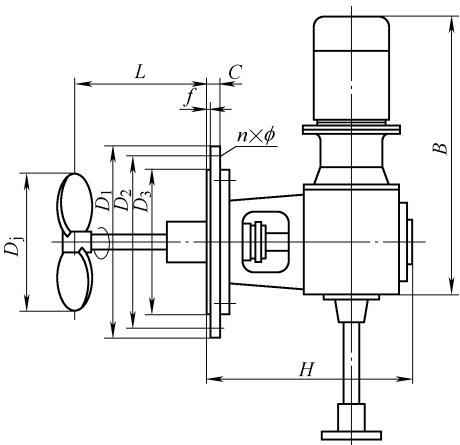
44 LZC 侧入式搅拌机外形尺寸
